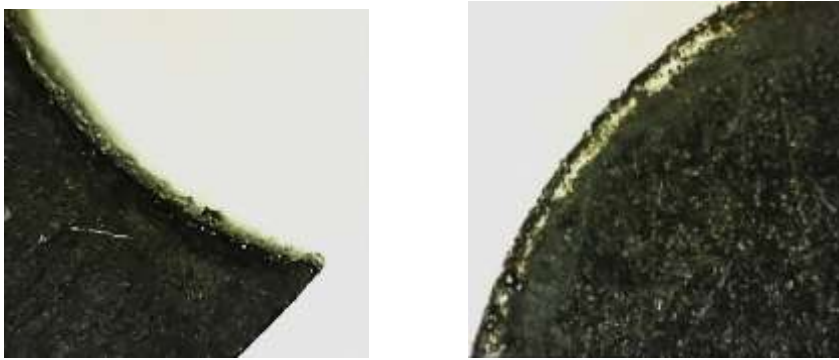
Верхня та нижня поверхні обробленої пластинки: з боку дії лазерного променя спостерігається більш широка смуга термодеструкції
